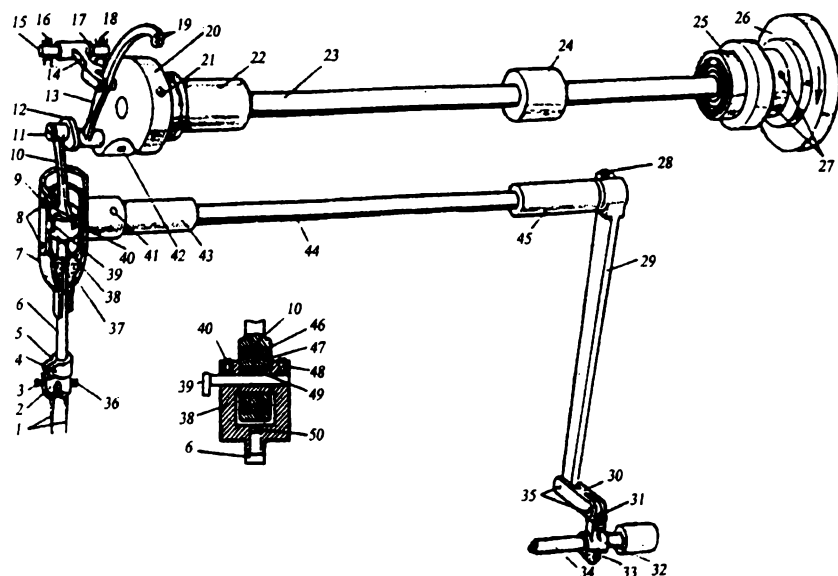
Конструкция механизма движения иглы машины 852 кл. ПМЗ
